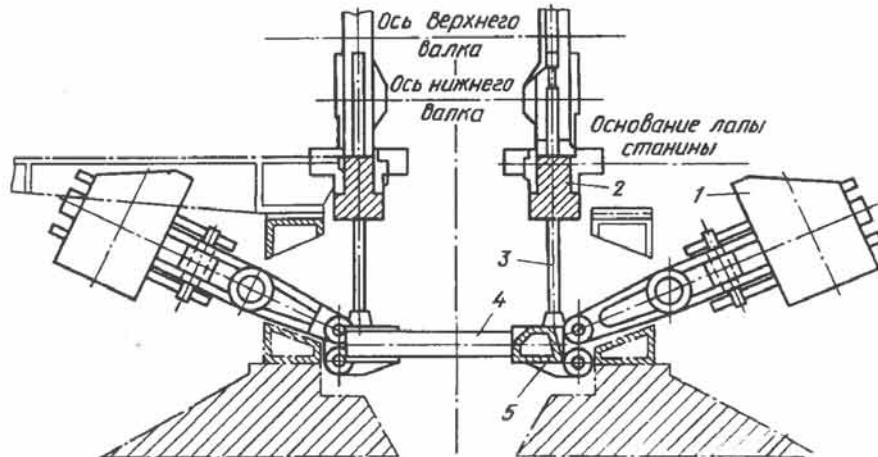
Грузовое уравновешивание верхнего вала блюминга: 1 — контргруз; 2 — клеть; 3 — вертикальные штанги; 4 — траверса; 5 — грузовые рычаги
